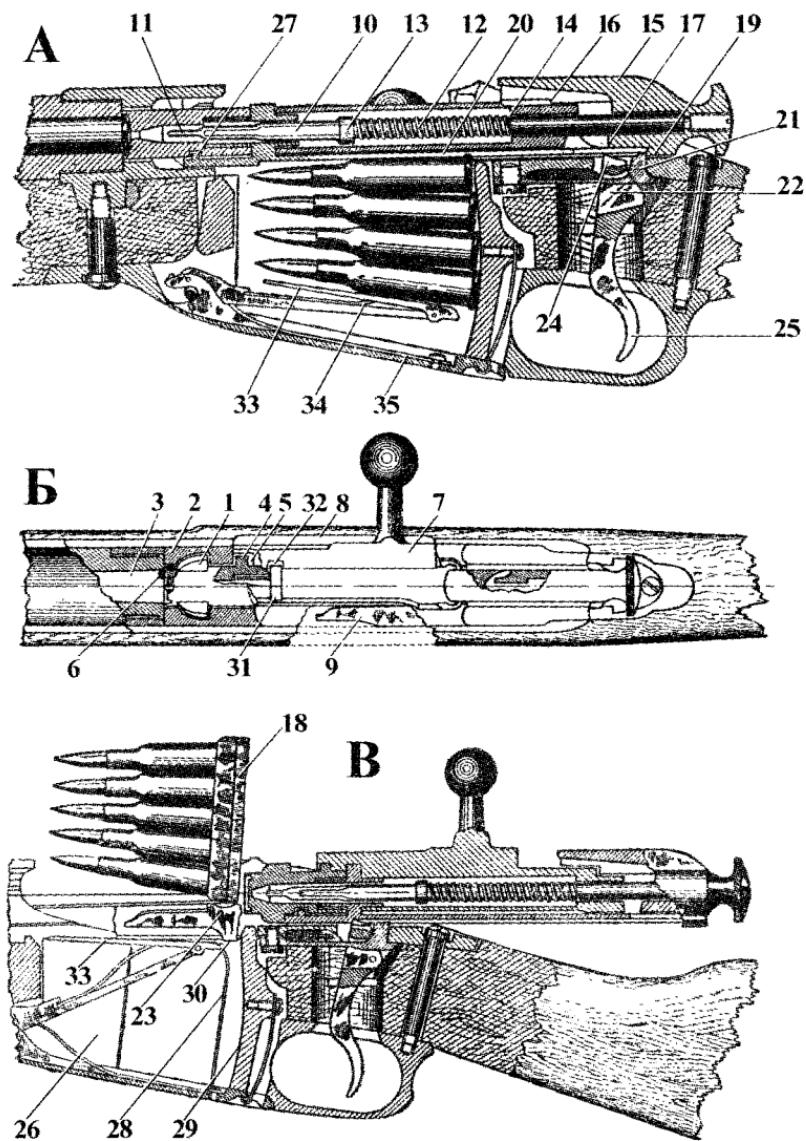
Положение деталей ударного и спускового механизмов винтовки Мосина обр. 1891/30 г..
